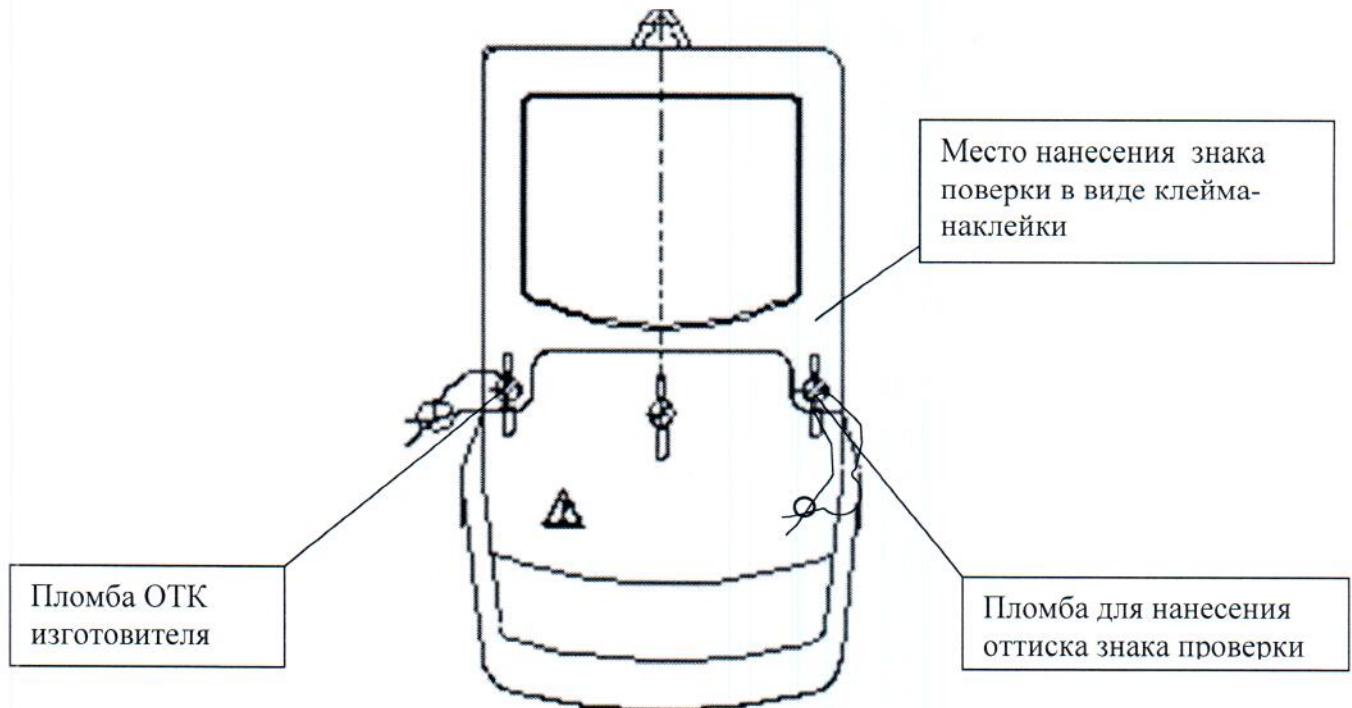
Корпус счетчиков СЕ102ВΥ SX XXX XXXXX
